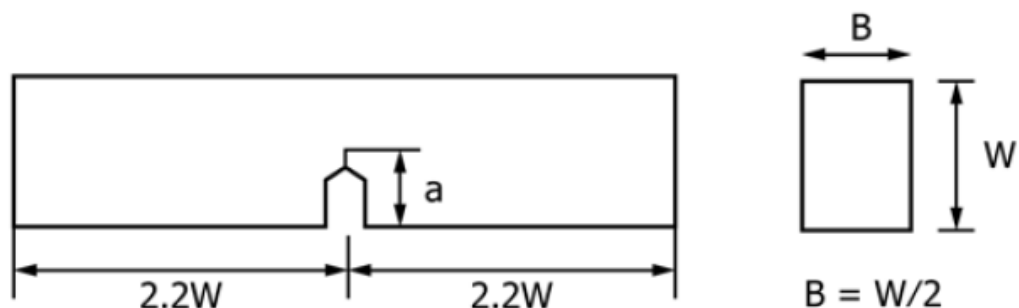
23 Dimensiones de probetas según ASTM D5045-14 [59]
